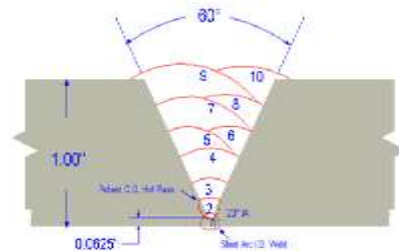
ESQUEMA DE JUNTA EN SOLDADURA DE TUBERÍA
